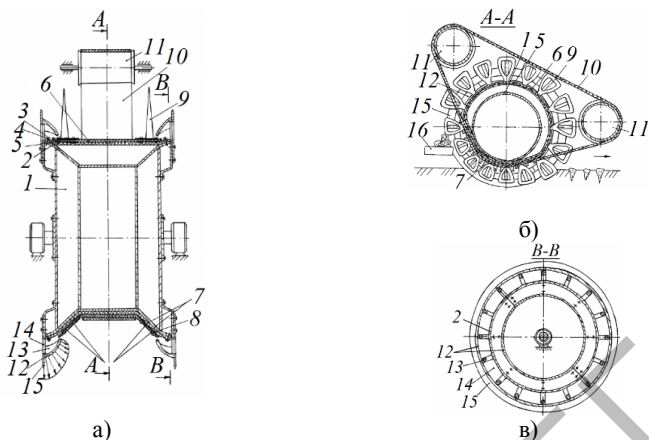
Выкапывающий рабочий орган корнеклубнеуборочной машины
